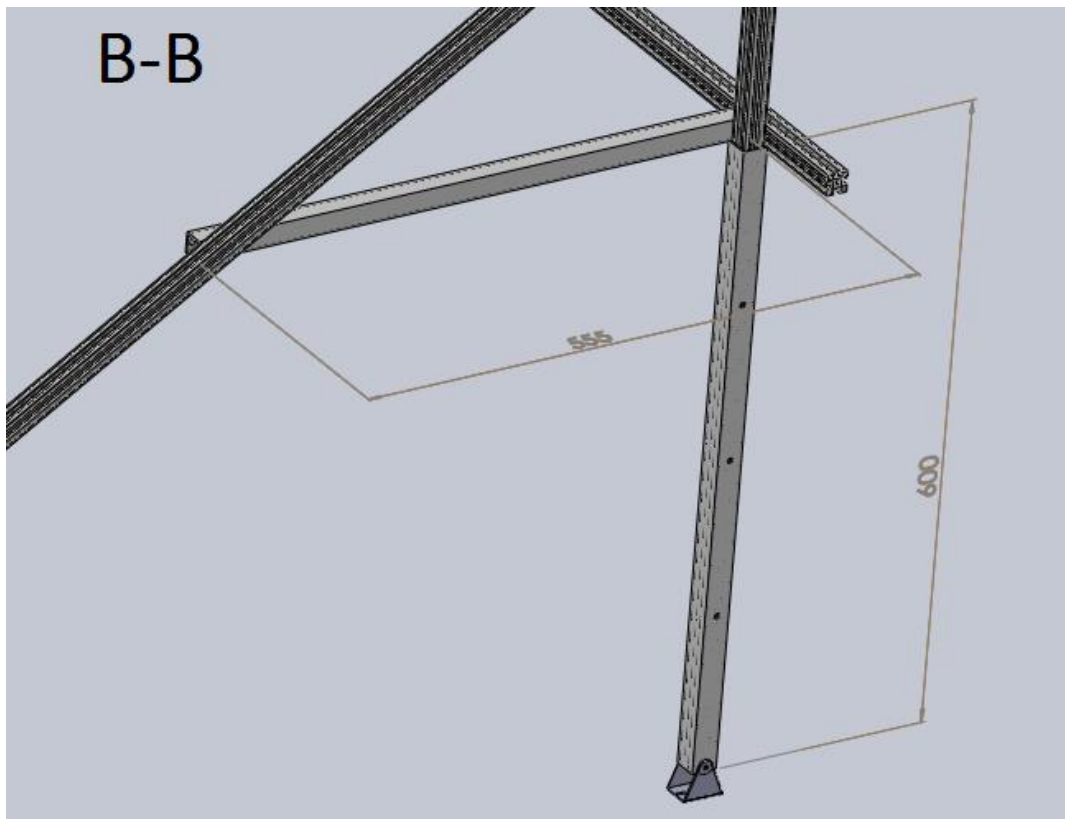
Desenho tridimensional do detalhe B-B, local onde se ajusta o ângulo do suporte de cobertura plana.
